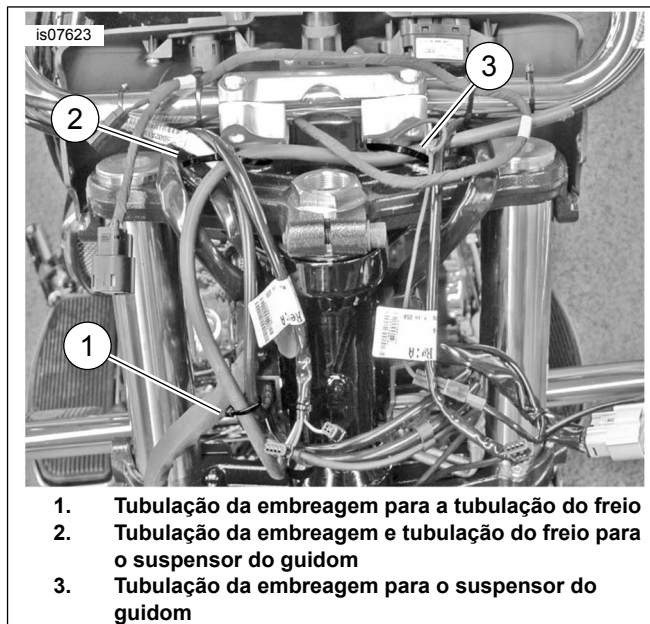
Tubulações de fluido de freio e da embreagem, modelos com carenagem (carenagem removida por motivos de clareza)
